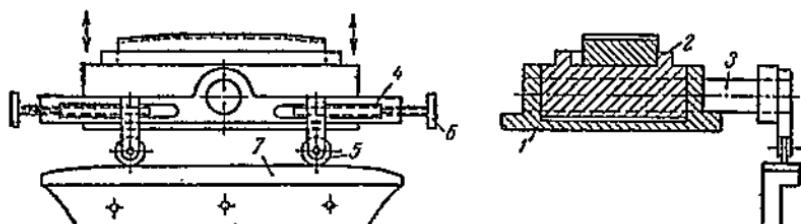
Приспособление фирмы Архимед для фрезерования плашек.
